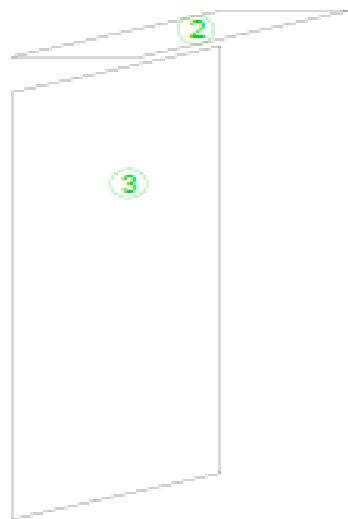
Сборка деталей 2 крыши и левой боковой части 3
